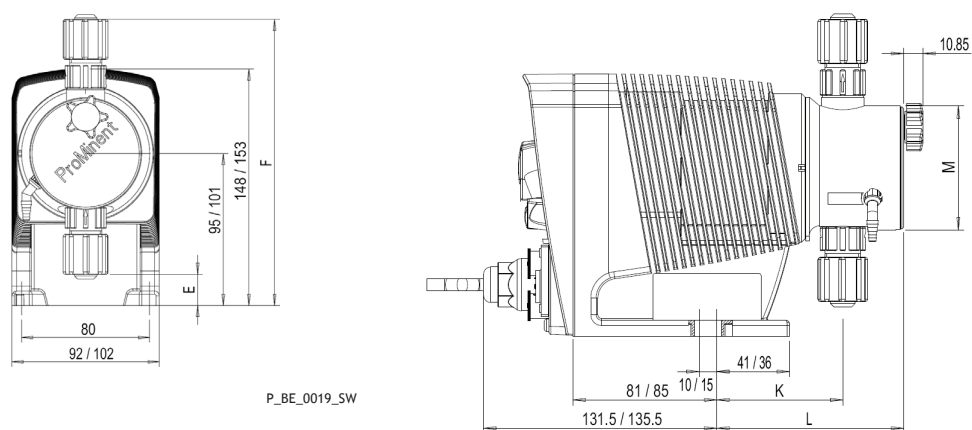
Размерный чертеж Beta® BT4b/BT5b, Материал конструкции PP
